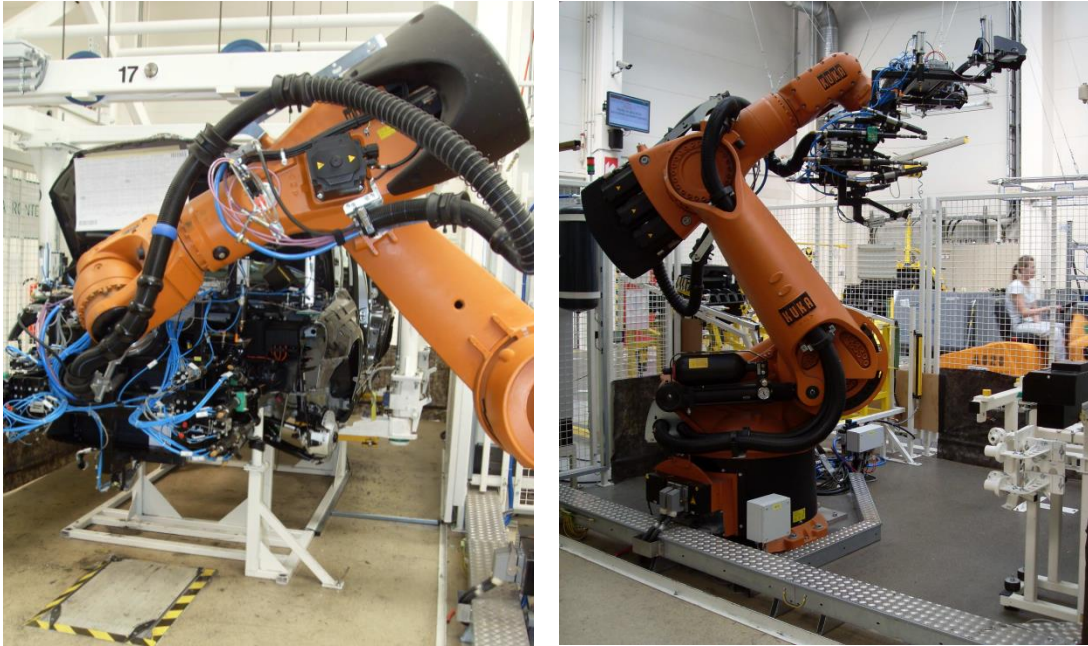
Obrábění robotem KUKA KR90 R2700 s vysokootáčkovým vřetenem Jäger Chopper 2300-40 HSK S5: a – broušení skla [57]; b – frézování umělého dřeva [58]
